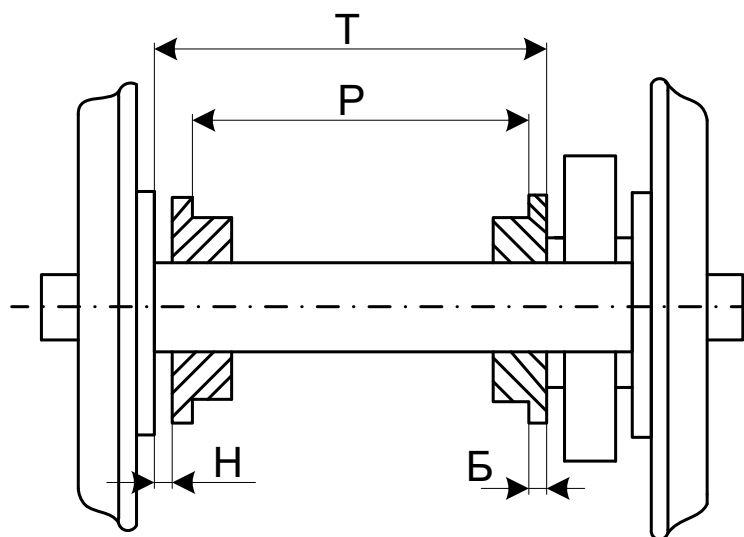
Схема определения размеров моторно-осевых подшипников
